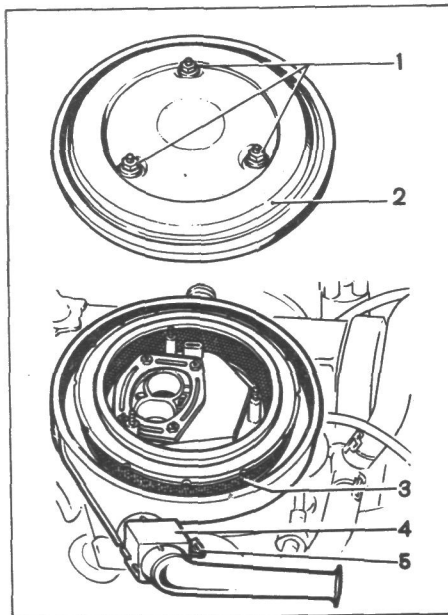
Воздушный фильтр: 1 — гайка; 2 — крышка; 3 — фильтрующий элемент; 4 — терморегулятор; 5 — ручка
